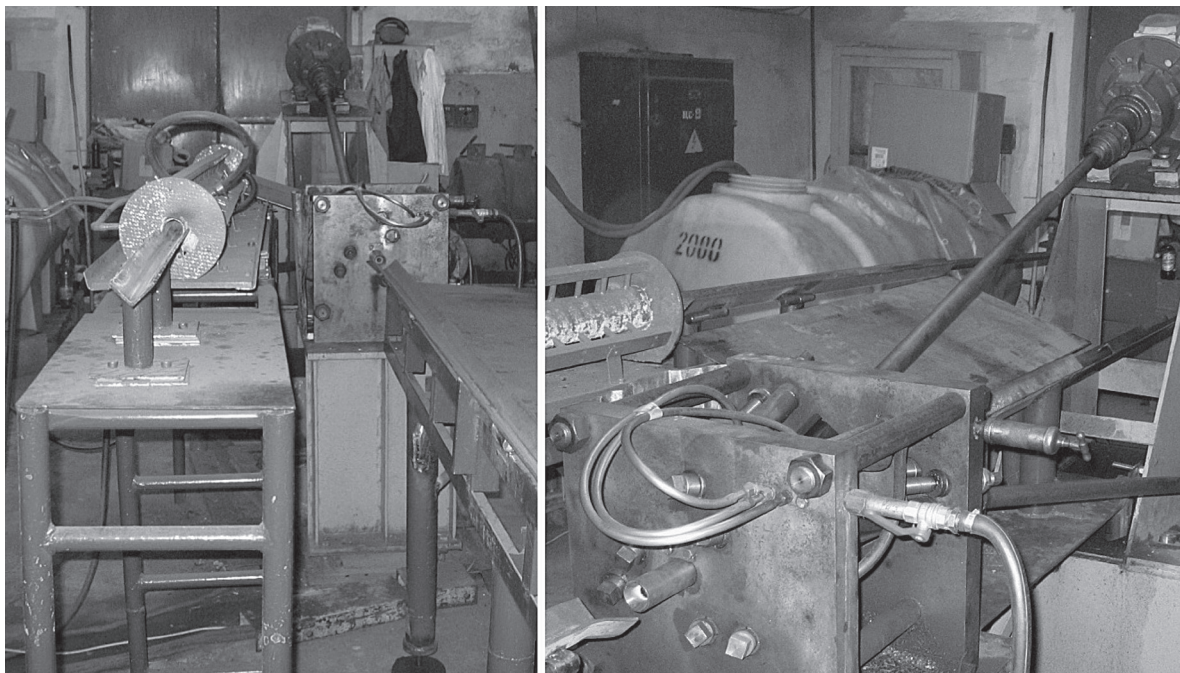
Трехвалковый стан поперечно-винтовой прокатки
